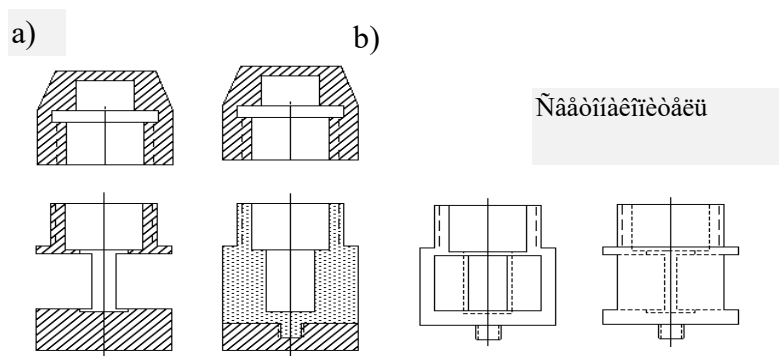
Держатель для виалы: а) медный держатель и б) медный держатель и крышка + тефлоновый светонакопитель.
